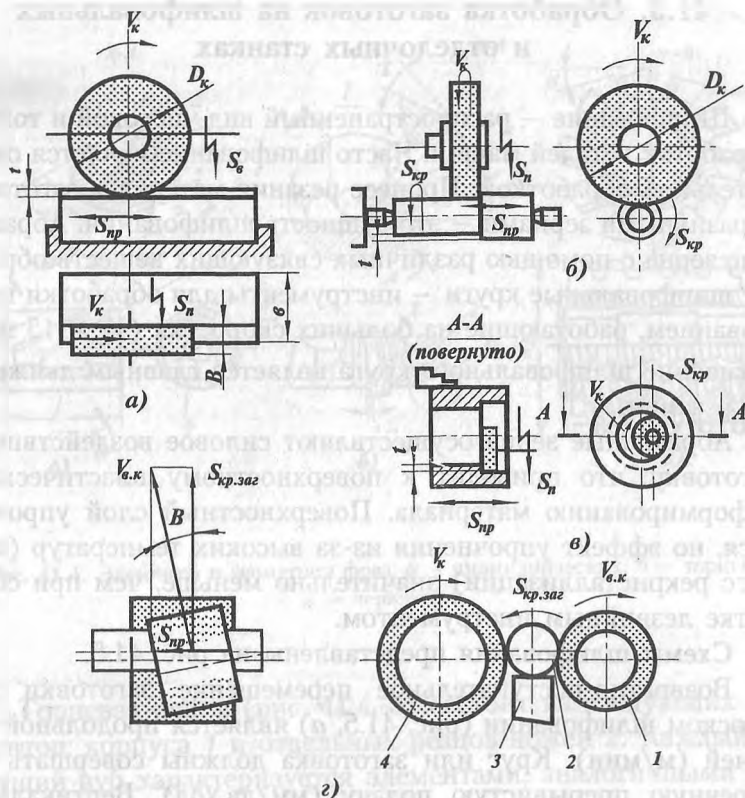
Основные схемы шлифования: а — плоское; б — круглое; в — внутреннее; г — бесцентровое
